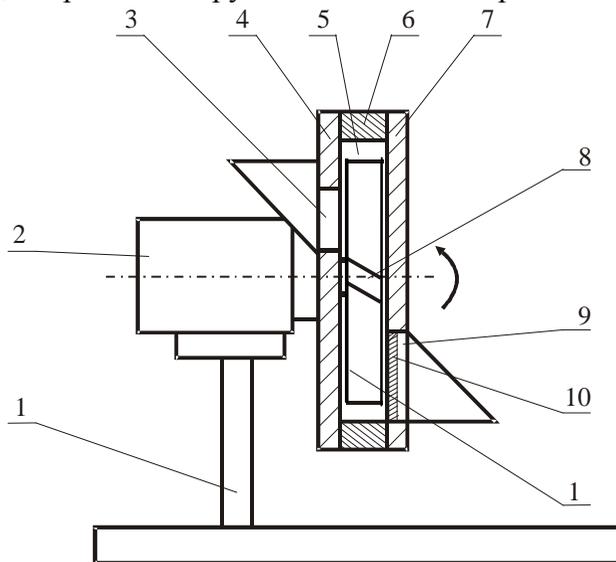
Общий вид дробилки: 1 – рама; 2 – электродвигатель; 3 – загрузочное окно; 4 и 7 – плиты; 5 – камера измельчения; 6 – барабан; 8 – ротор; 9 – выгрузное окно; 10 – решето; 11 – лопасти
